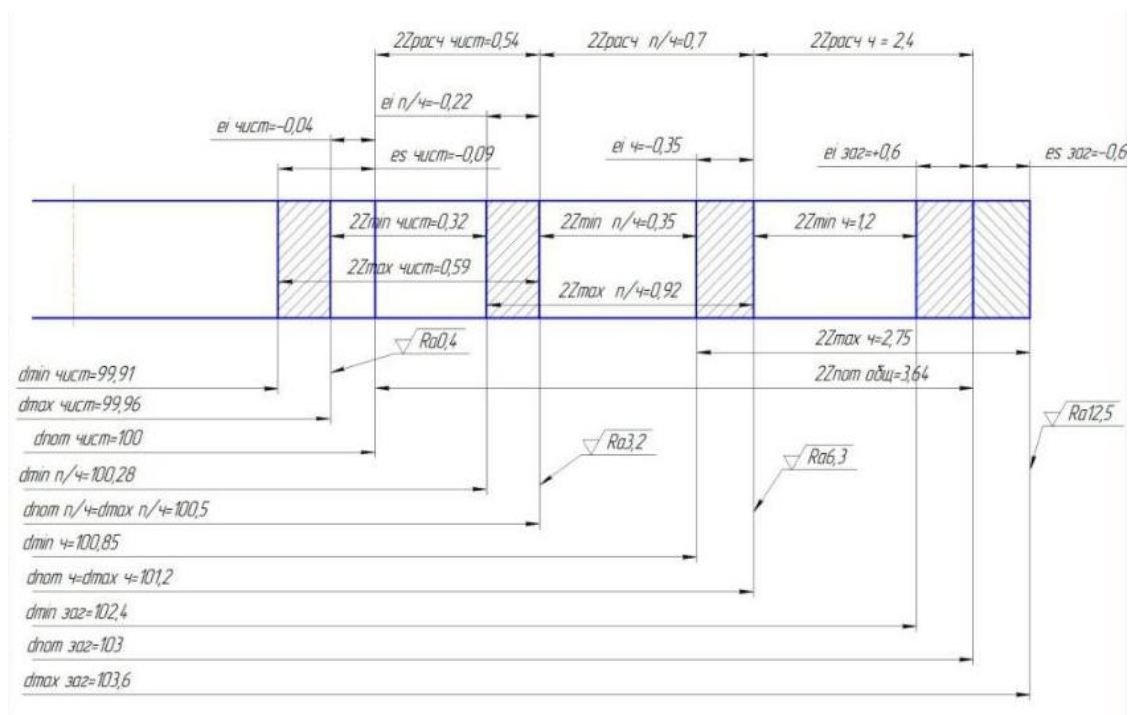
Схема розташування припусків і допусків на виготовлення
